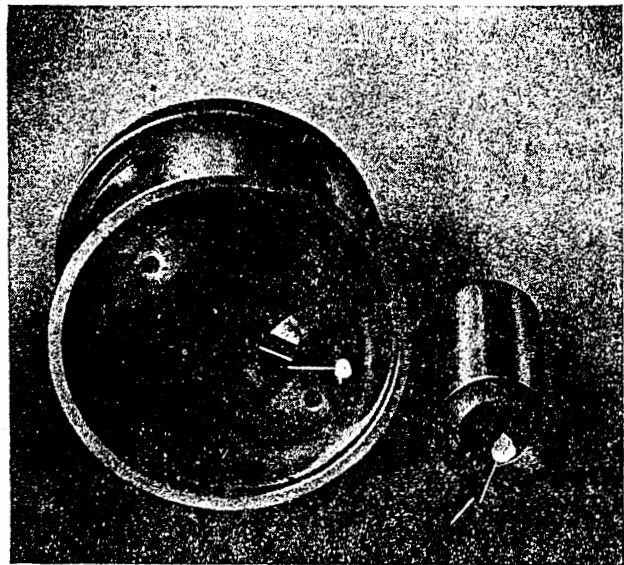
Kennzeichnung der Sortierungsgruppen auf Kolben und Kolbenbolzen
